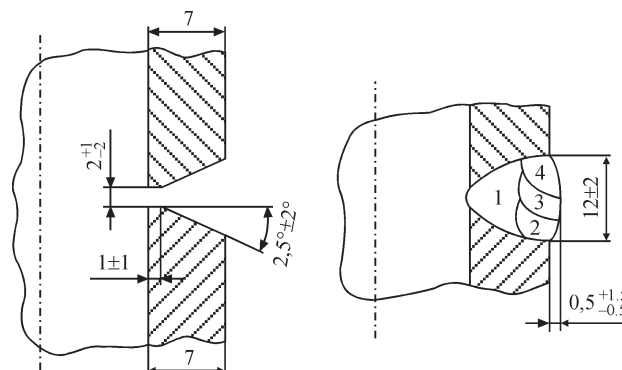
Підготовка кромки одного U-типу для зварних з'єднань труб (процес зварювання SMAW) (а), передбачувана конфігурація зварного шва та розташування зварних валиків (б)
